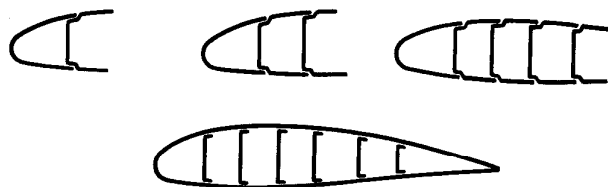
Схема сборки при сварке крыла из профилированных секций
